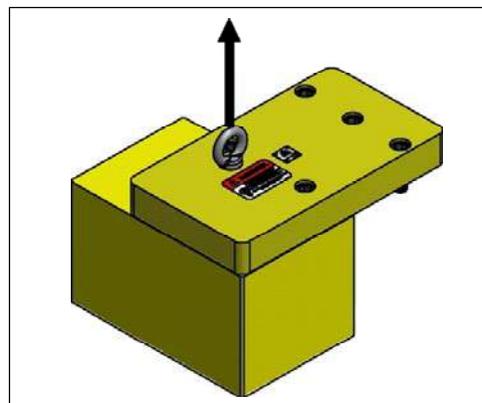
ADAPTADOR DE CONTRAPESO DE ELEVACIÓN MONTAJE
